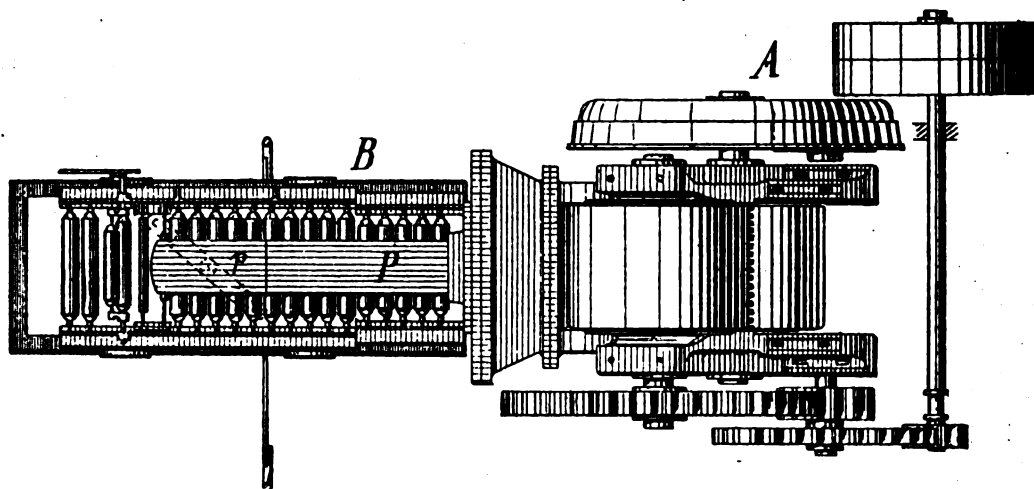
Grundriss einer horizontalen Packet-Dachziegelpresse.
